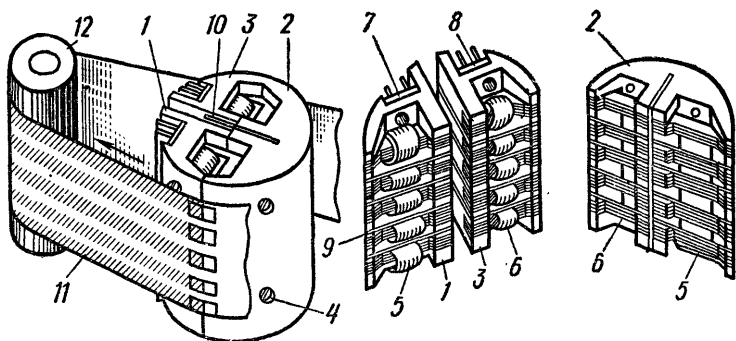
Устройство многодорожечного блока комбинированных головок.
